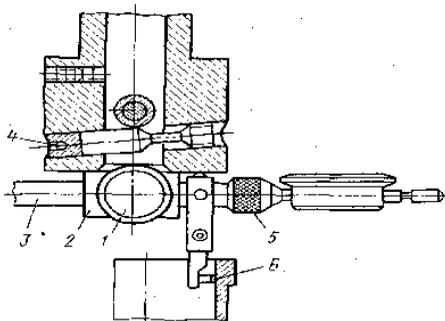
Резцовая головка 2А78Н с приспособлением для центрирования гильз:
